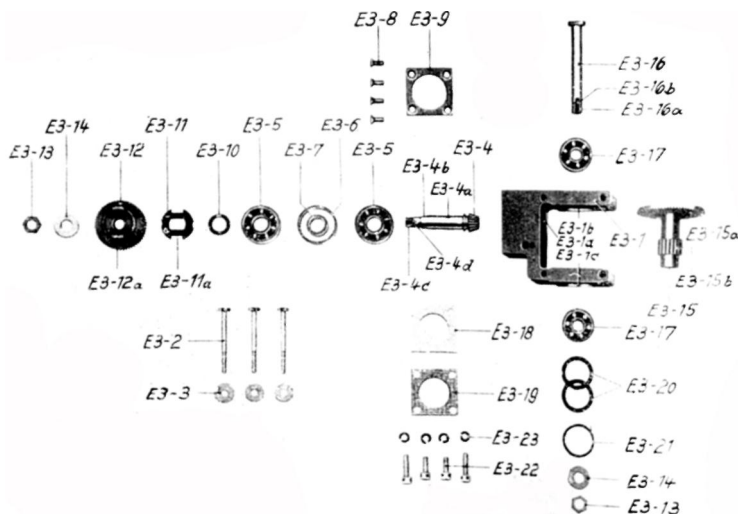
ED 151 B; Zahnradgetriebe; Einzelteile
